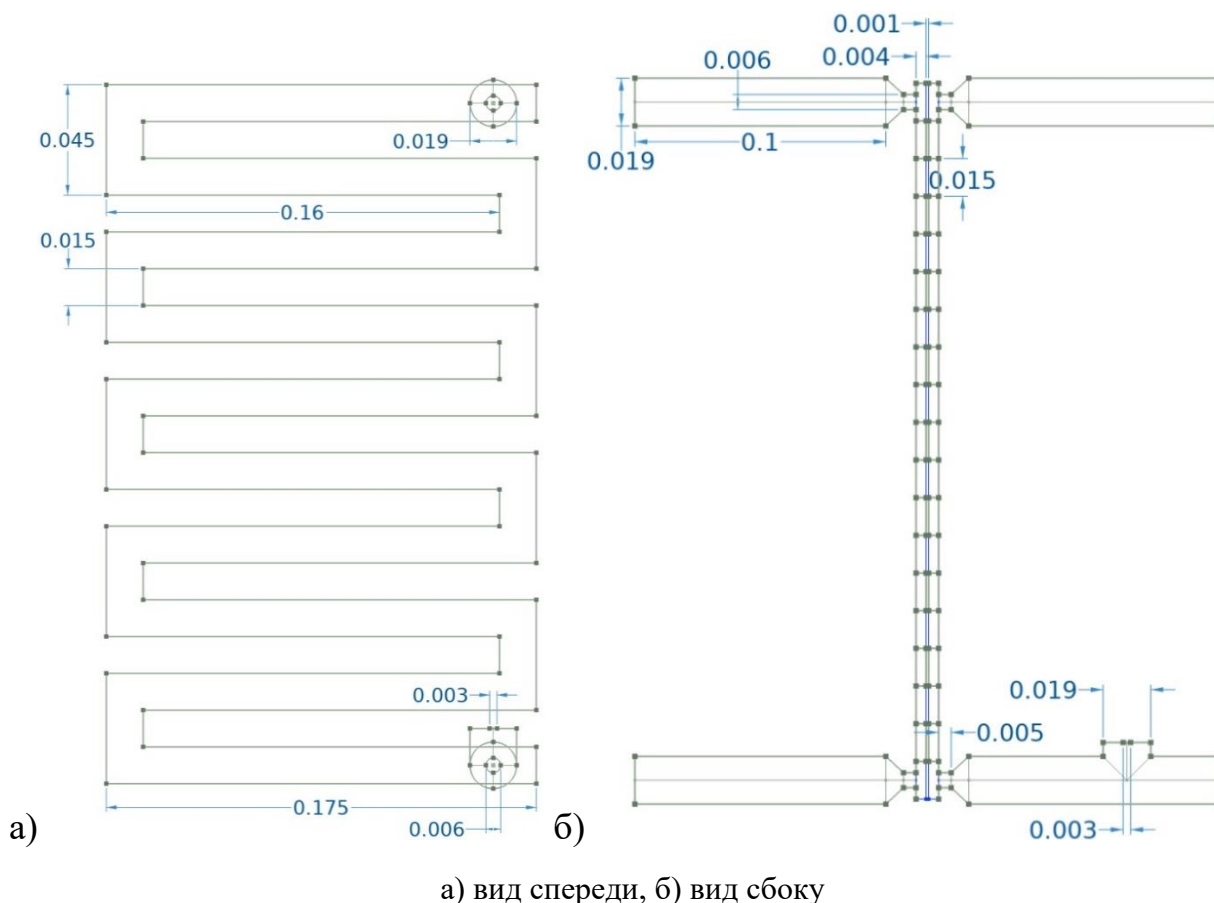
Чертеж общего вида модели электроактиватора для профилактической обработки ульев
